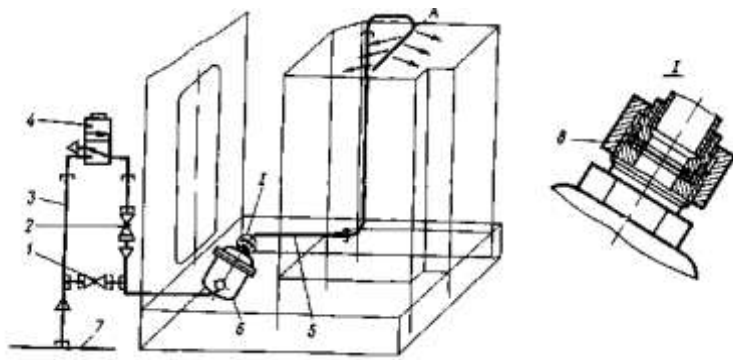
Схема установки порошкового пожаротушения высоковольтной камеры:
